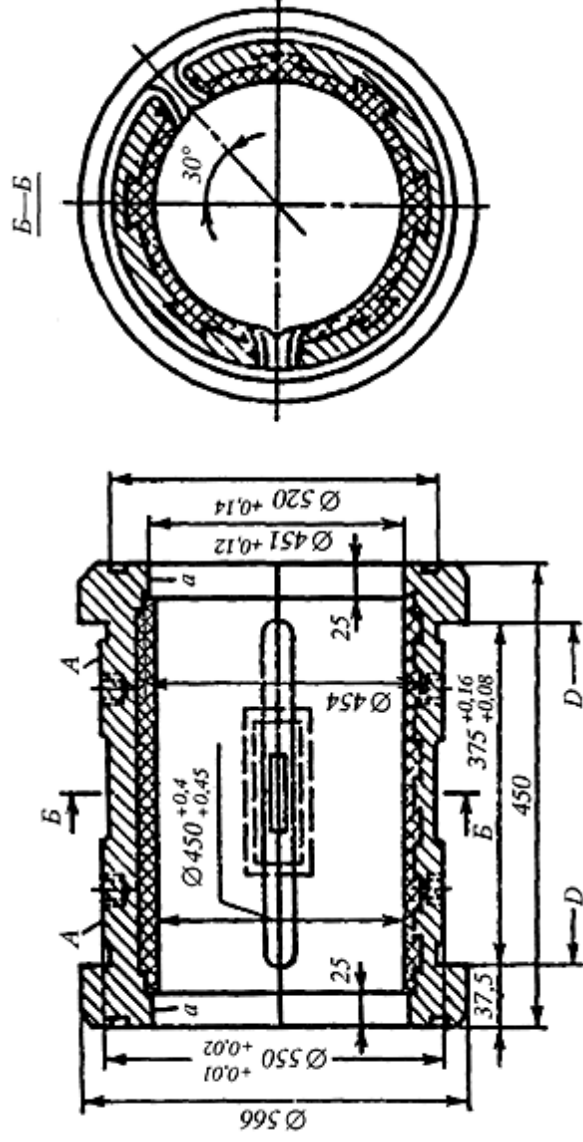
Нерегулируемый вкладыш опорного подшипника
